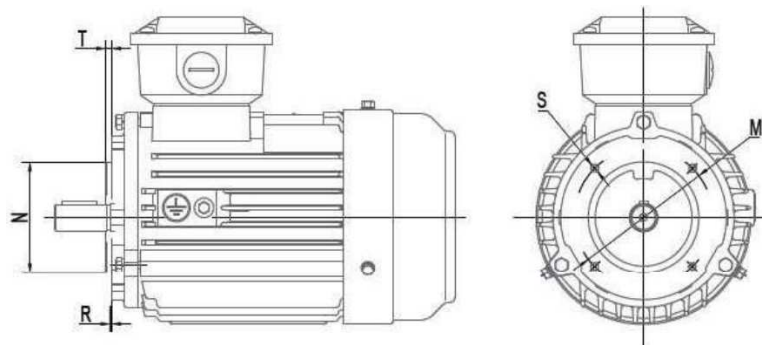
Esquema del montaje IM B14 seleccionado. El motor quedará vinculado directamente al reductor.
